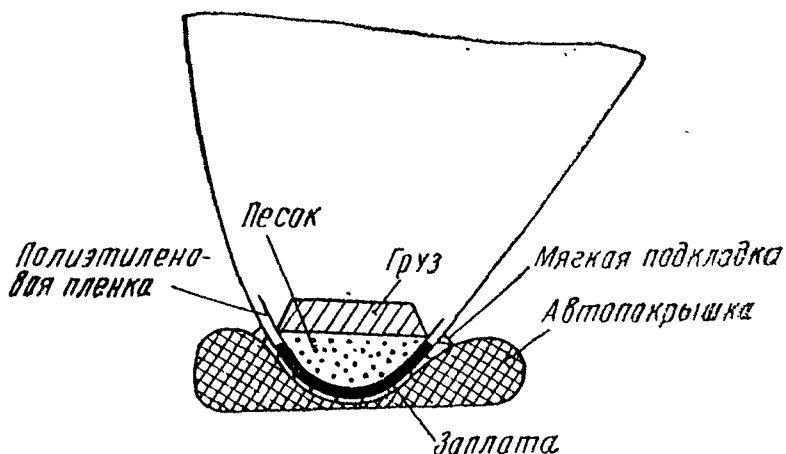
Установка обтекателя и схема наложения груза при ремонте
